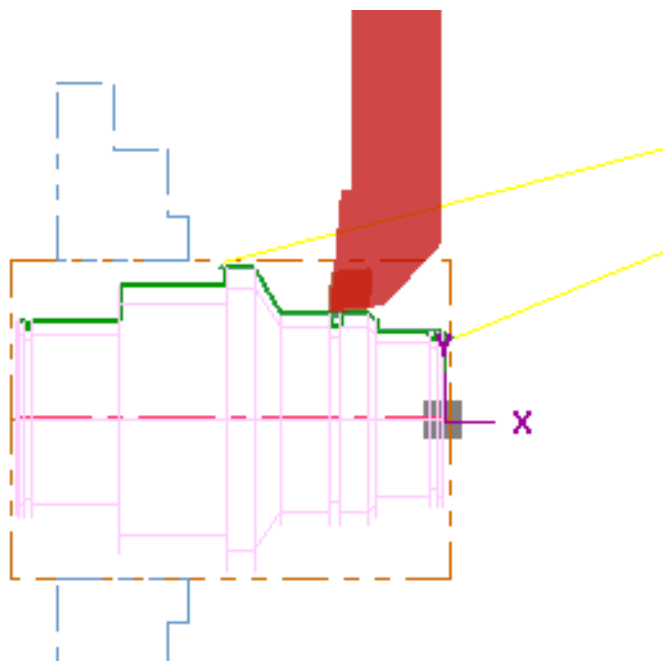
Definice polotovaru a upnutí první strany
